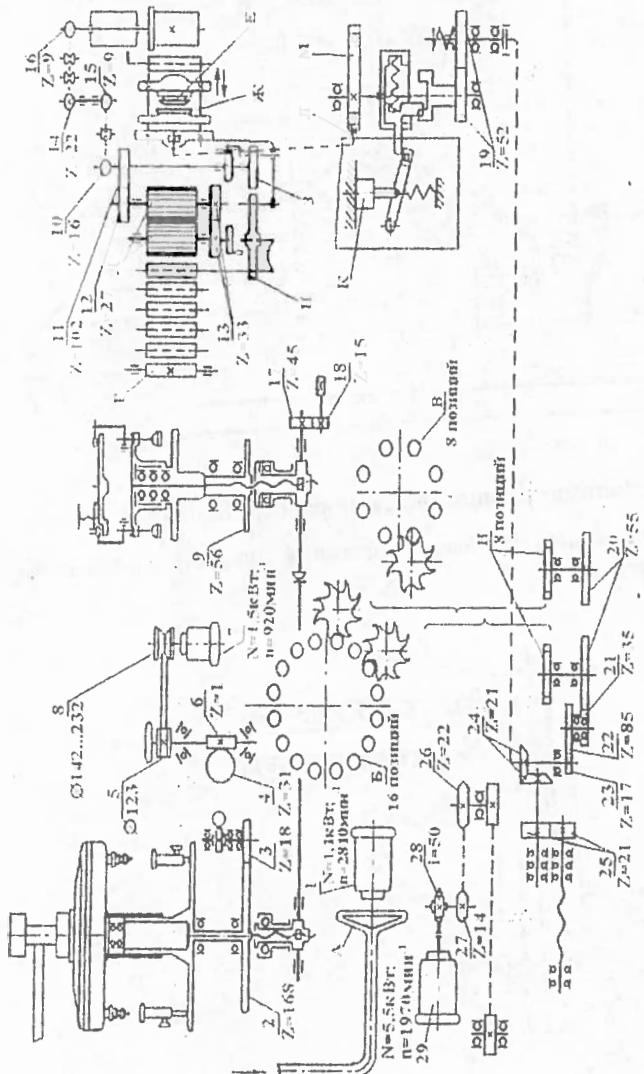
Кинематическая схема агрегата Е2-ОПВ-3
